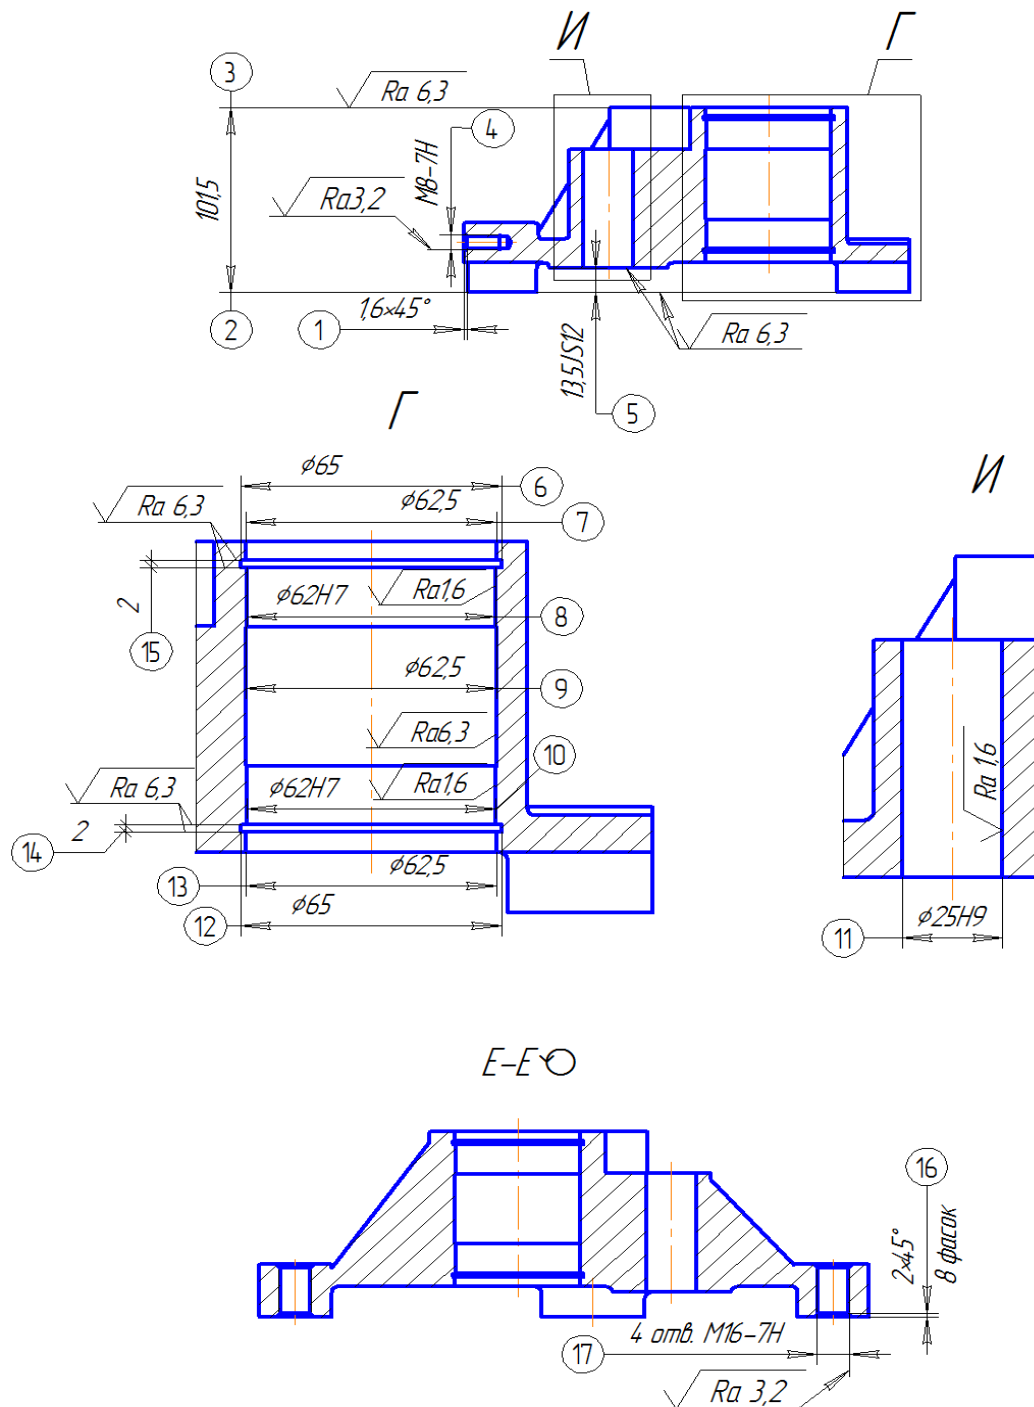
Эскиз детали «Корпус подшипника тягового механизма»
